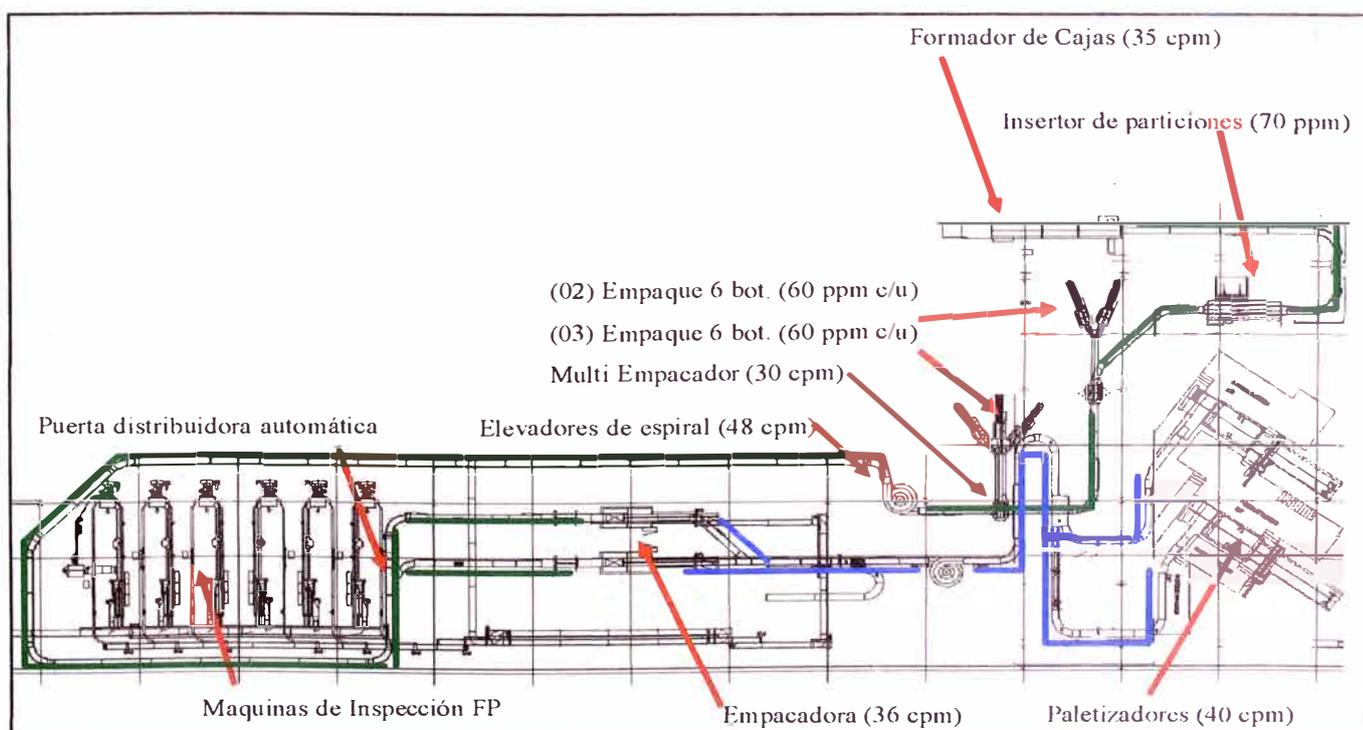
Vista de planta del sistema de transportadores de caja.
